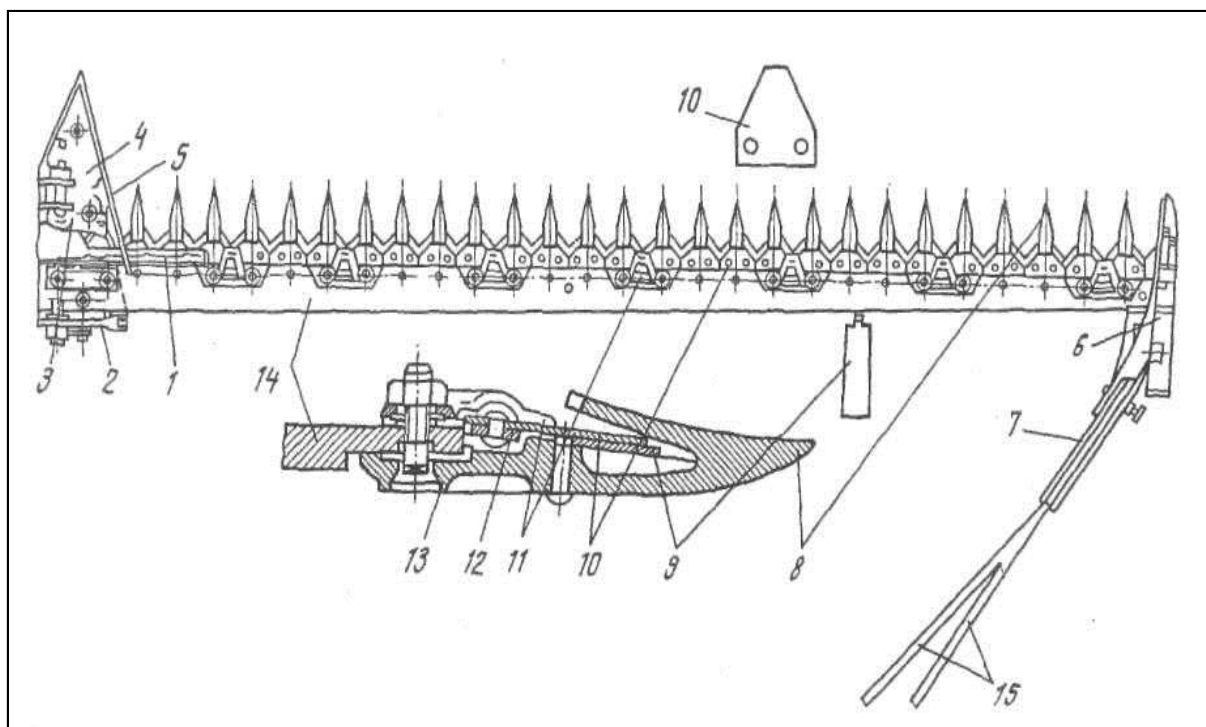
Режущий аппарат косилок КС-Ф-2,1, КД-Ф-4,0, КП-Ф-6,0: 1 – головка ножа; 2 – направляющая головки ножа (задняя); 3 – крышка головки ножа (передняя); 4 – башмак внутренний; 5 – делитель; 6 – башмак наружный; 7 – доска полевая; 8 – палец; 9 – противорежущая пластина; 10 – сегмент ножа; 11 – прижимная лапка; 12 – спинка ножа; 13 – пластина трения; 14 – пальцевый брус; 15 – отводные прутки
